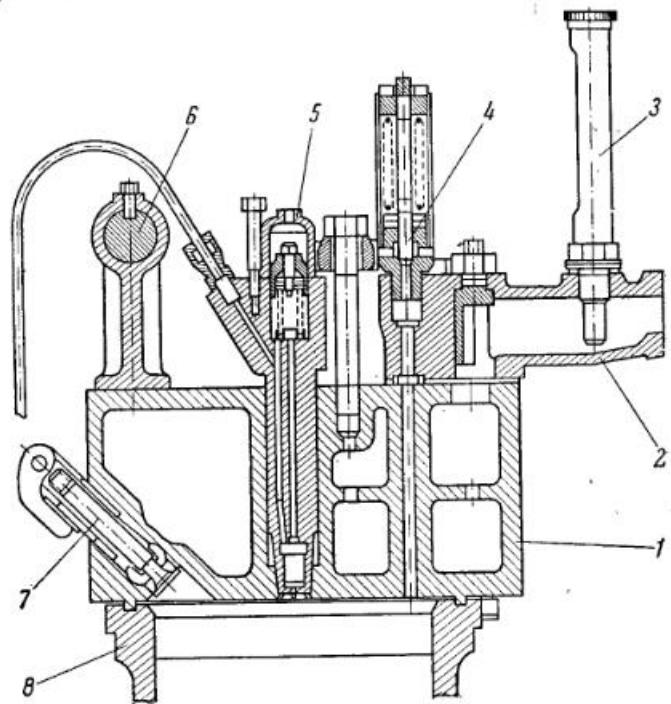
Крышка цилиндра двигателей типа NVD-24 в комплекте с оборудованием:
